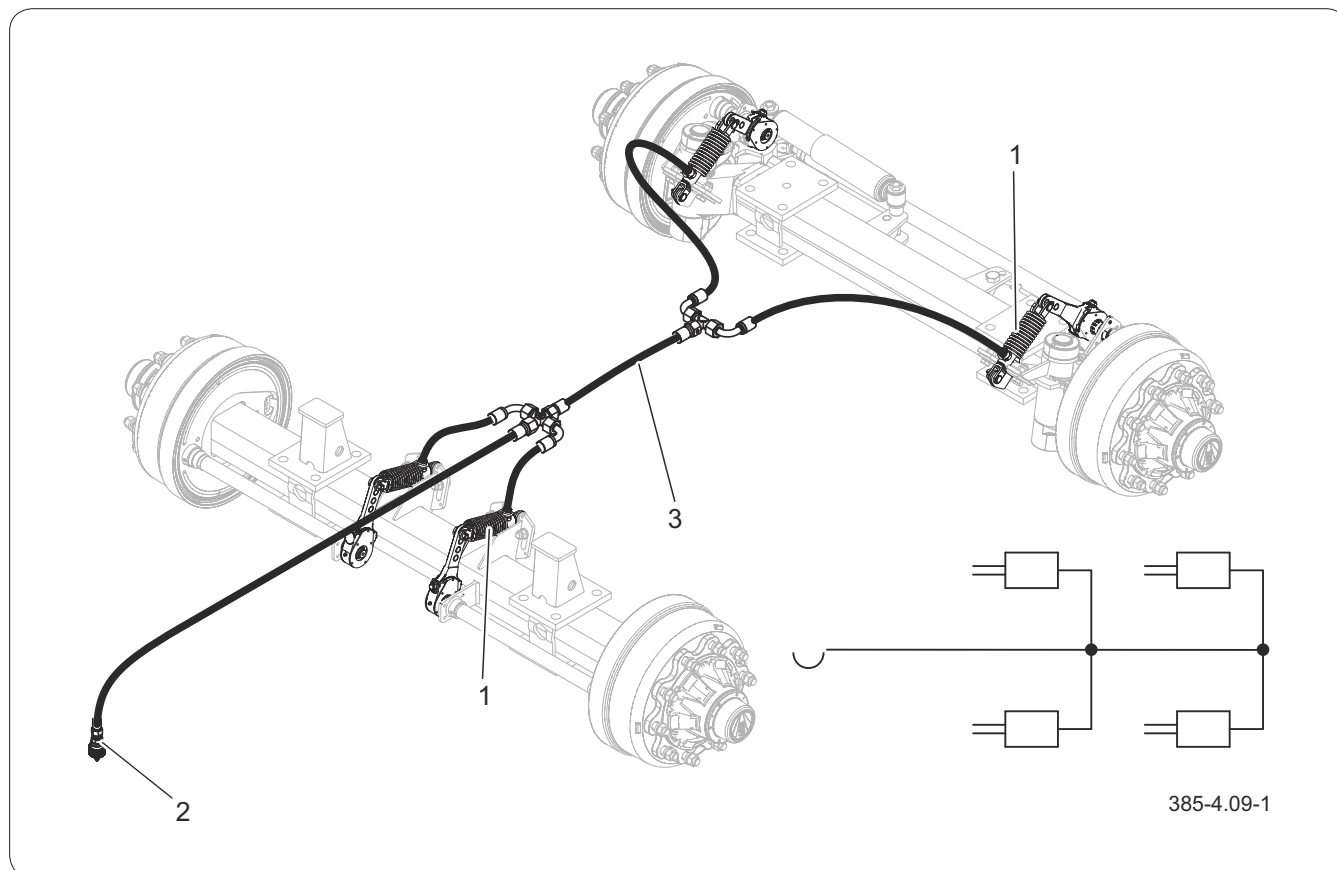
Schema und Aufbau der hydraulischen Bremsanlage (FR)
